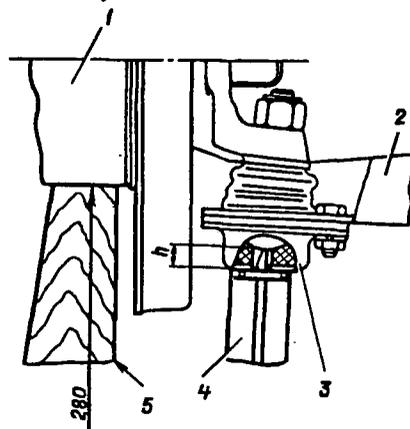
Схема проверки нижних шаровых шарниров: 1 - ступица колеса; 2 - нижний рычаг; 3 - нижний шаровой шарнир; 4 - штангенциркуль; 5 - деревянная колодка
